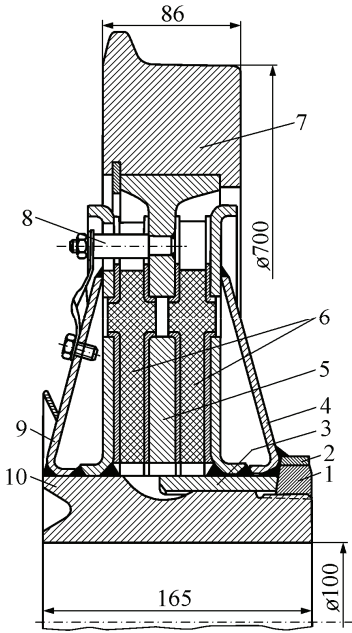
Прорезиненное колесо трамвая: 1 – гайка; 2 – планка; 3 – втулка с внешним диском; 4 – внешний диск; 5 – колесный центр; 6 – упругие диски; 7 – бандаж; 8 – болтовое соединение; 9 – внутренний диск; 10 – ступица с внутренним диском
